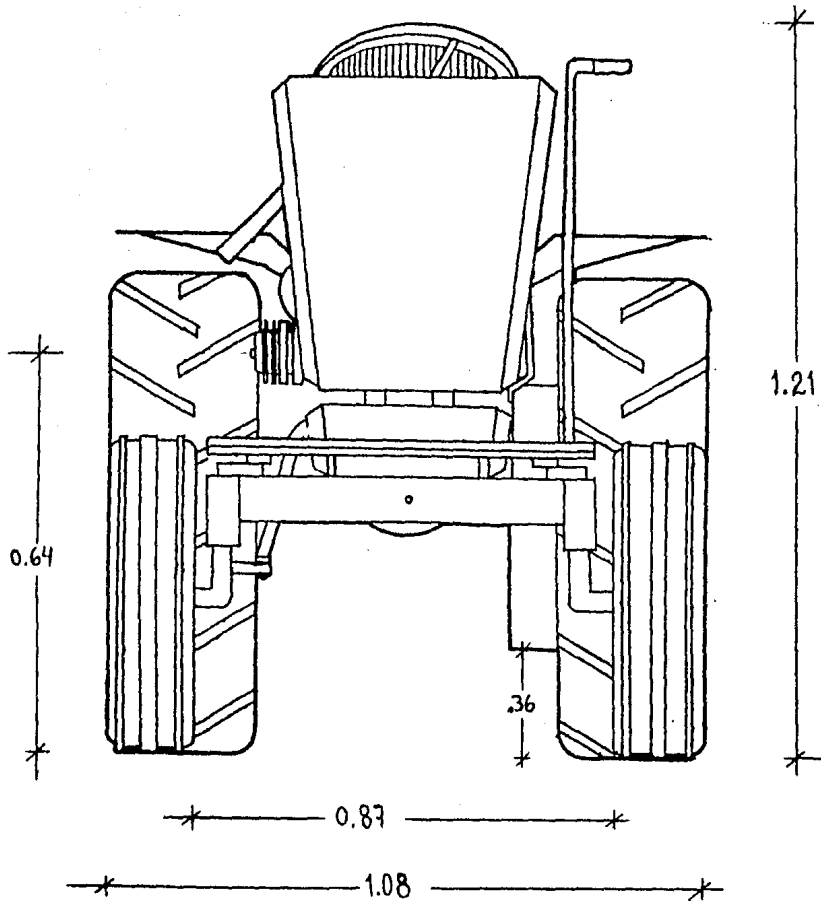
Dimensiones del minitractor. Vista frontal. (m)
